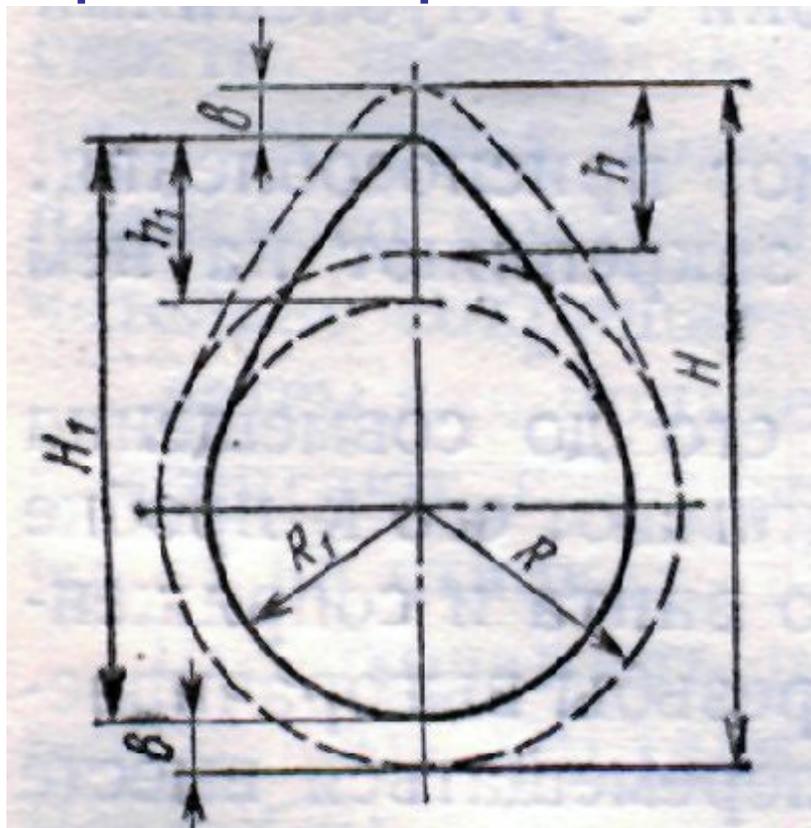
Кулачок распределительного вала, прошлифованный под ремонтный размер с сохранением профиля
